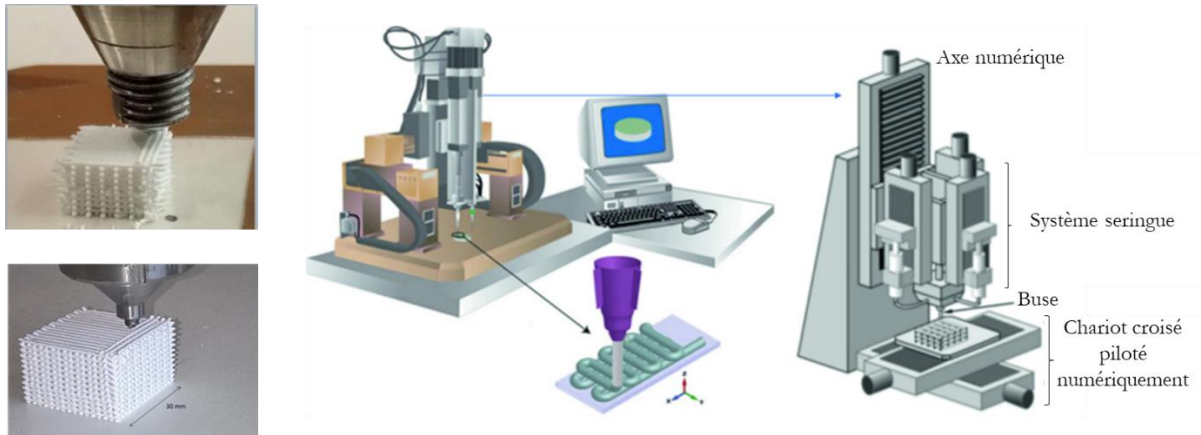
Exemples d'une technologie de robocasting pour céramiques [101]
